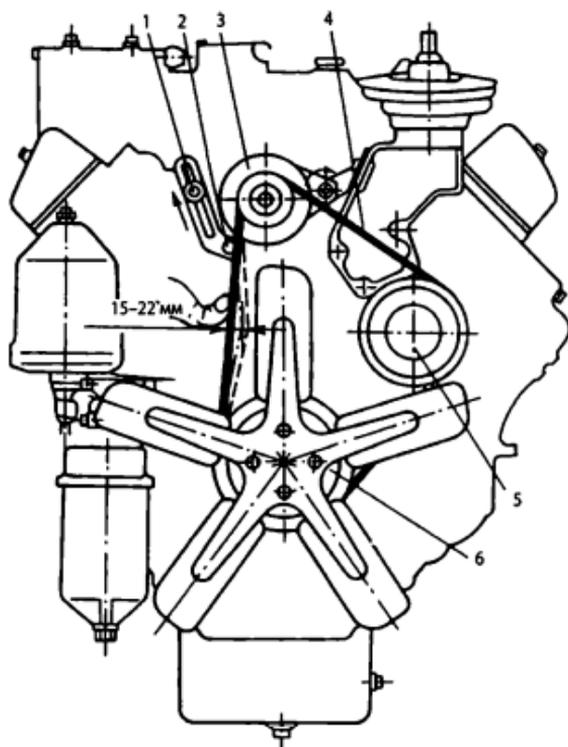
Перевірка і регулювання натягу паса вентилятора
